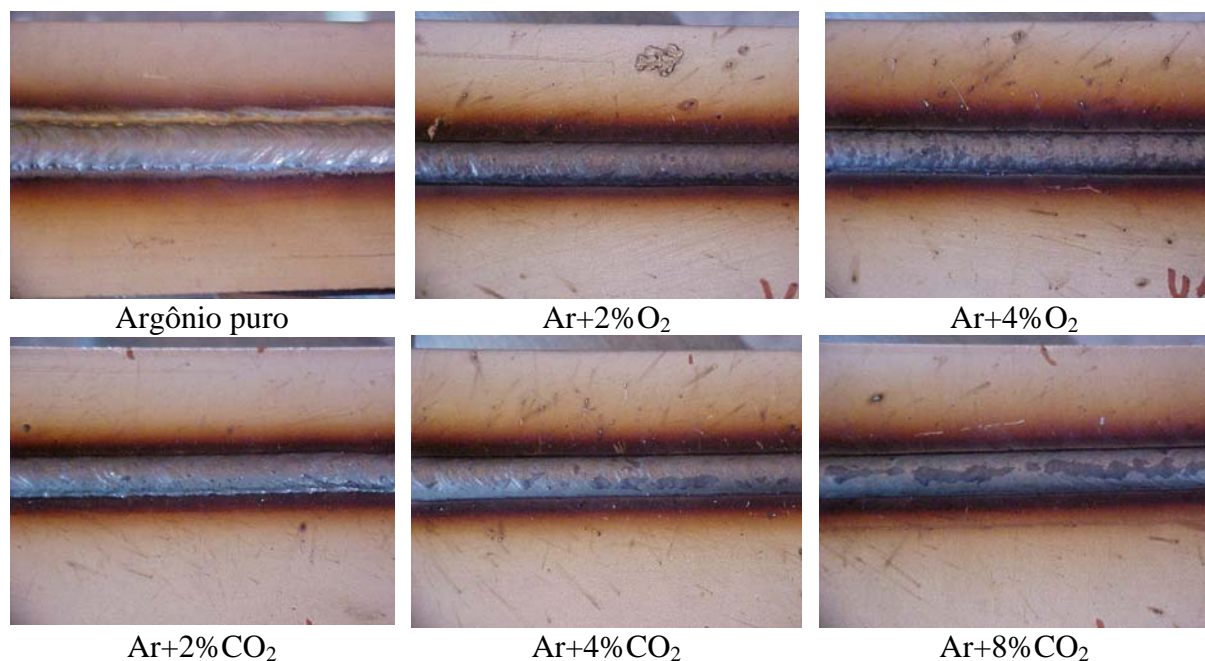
Aspecto do cordão de solda para o arame eletrodo ER430.
